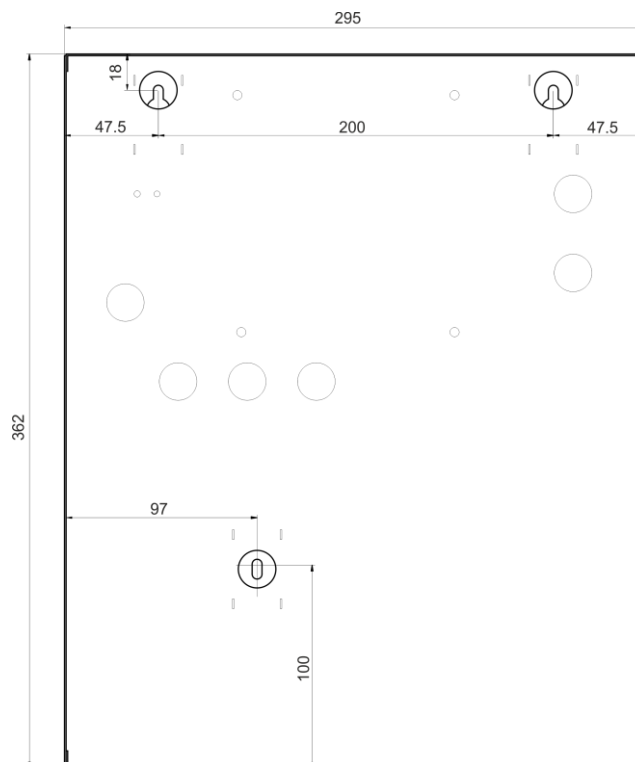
Установочный чертеж ППКПиУ «Бирюза-М»
